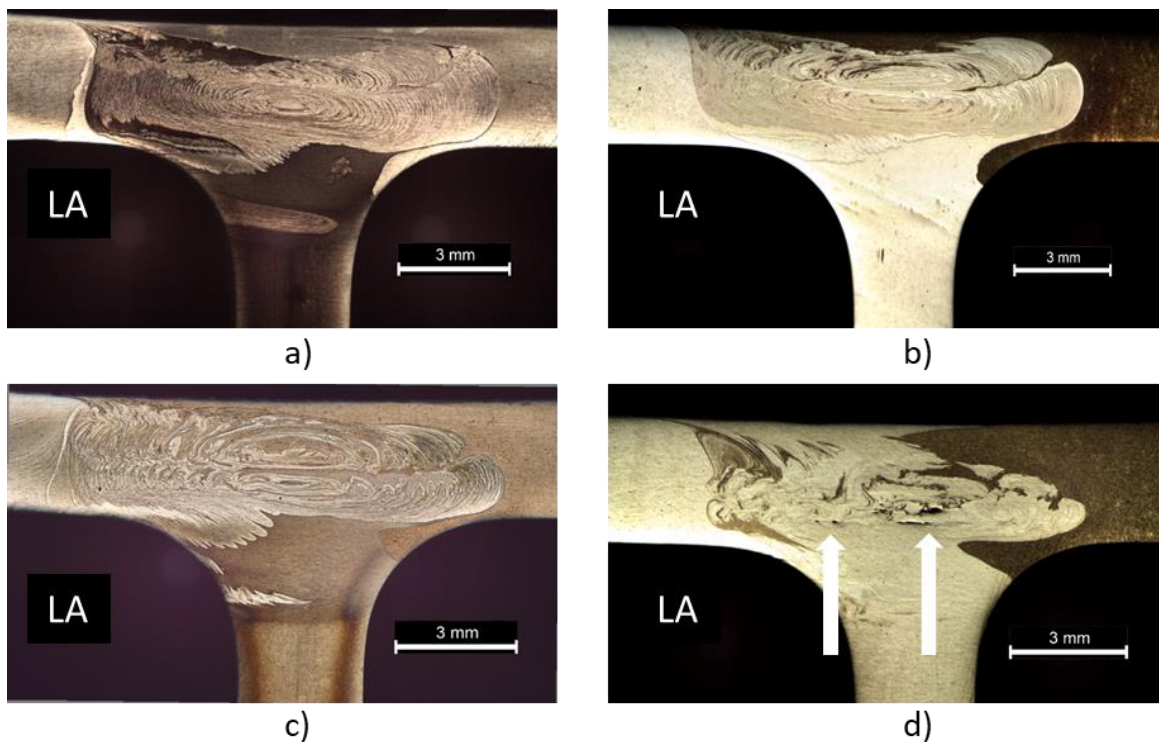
Macrografias das soldaduras: a) 562-30-F (Weck); b) 562-60-F (Keller modificado); c) 562-120-F (Weck); d) 562-280-F (Keller modificado).
